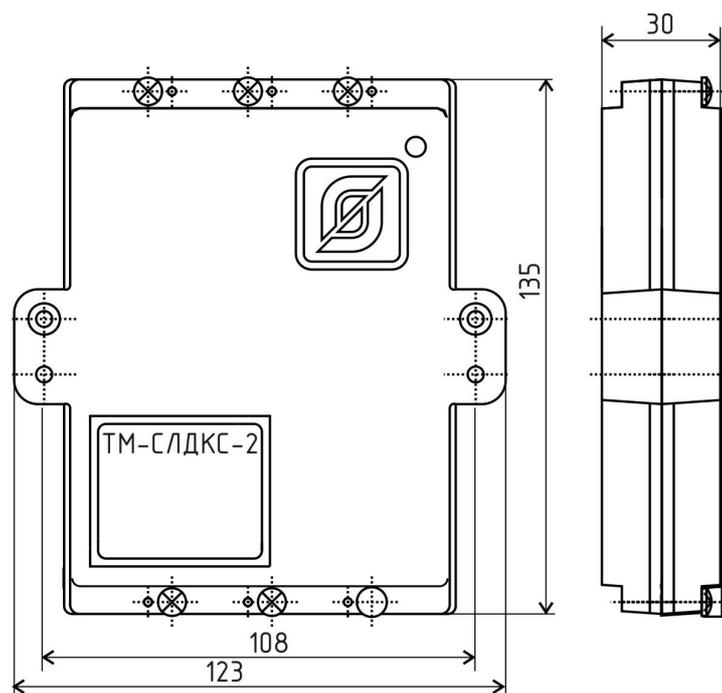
Габаритные размеры ТМ-СЛДКС-2
